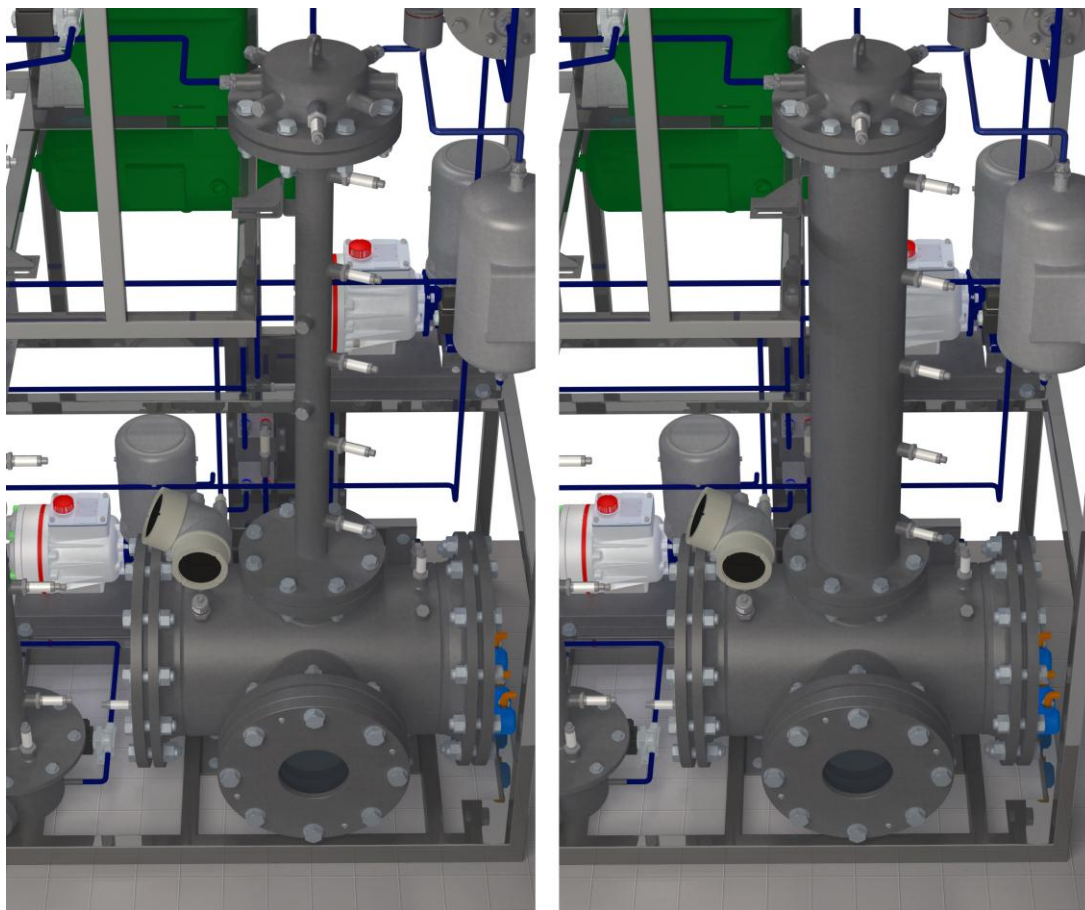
Zapojení stripovací kolony (šedě - neaktivní potrubí)
